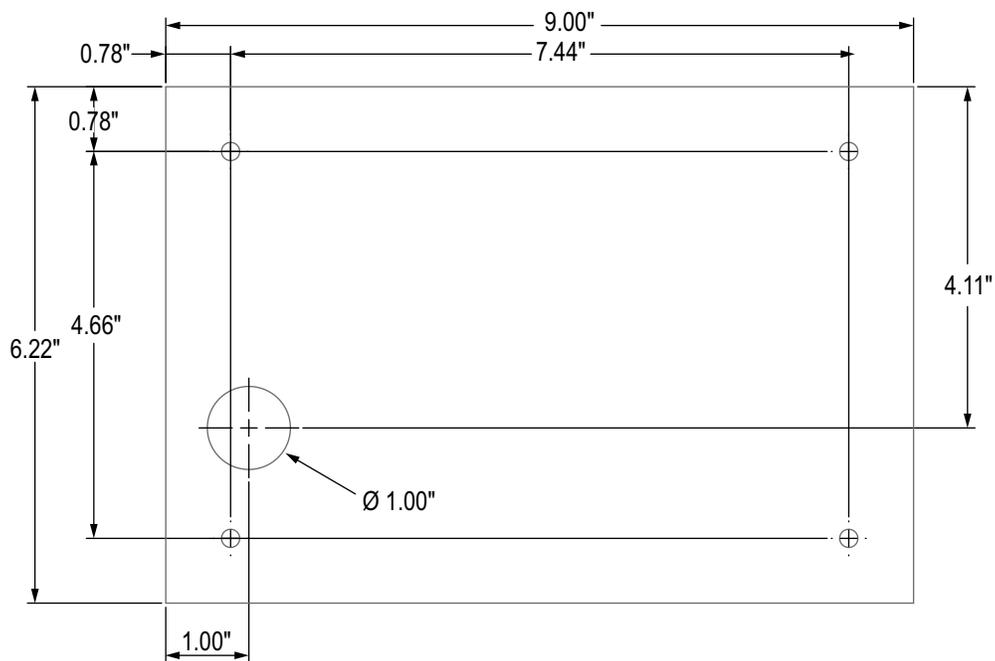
Dimensioni della versione da 7" con montaggio a pannello solo touch
